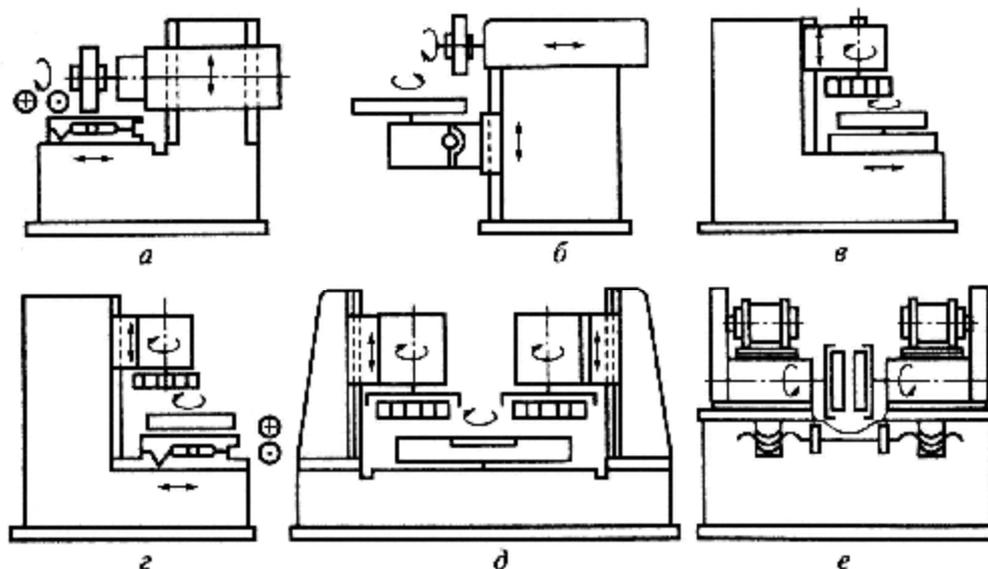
Схемы движения рабочих органов плоскошлифовальных станков: а, б – с горизонтальными шпинделями; в, г – с вертикальными шпинделями; д, е – двухшпиндельные для шлифовки торцами кругов (с вертикальными и горизонтальными шпинделями)
